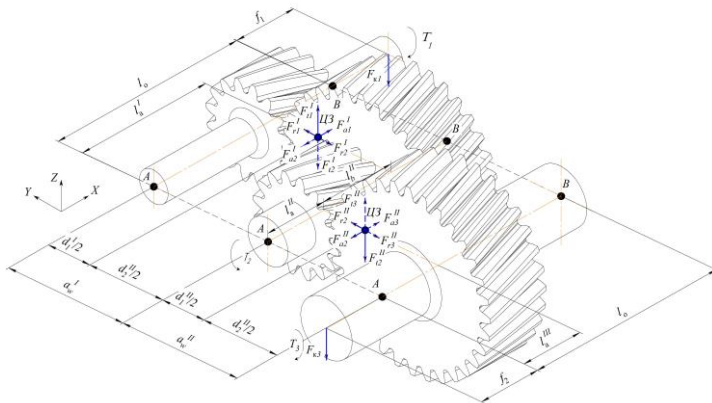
К компоновке цилиндрического двухступенчатого редуктора
